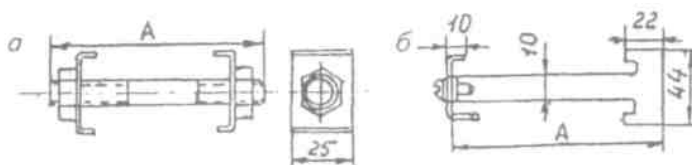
Распорные прокладки: а — распорная прокладка из круговой стали типа ПР; б — штампованная распорная прокладка типа ПРШ
